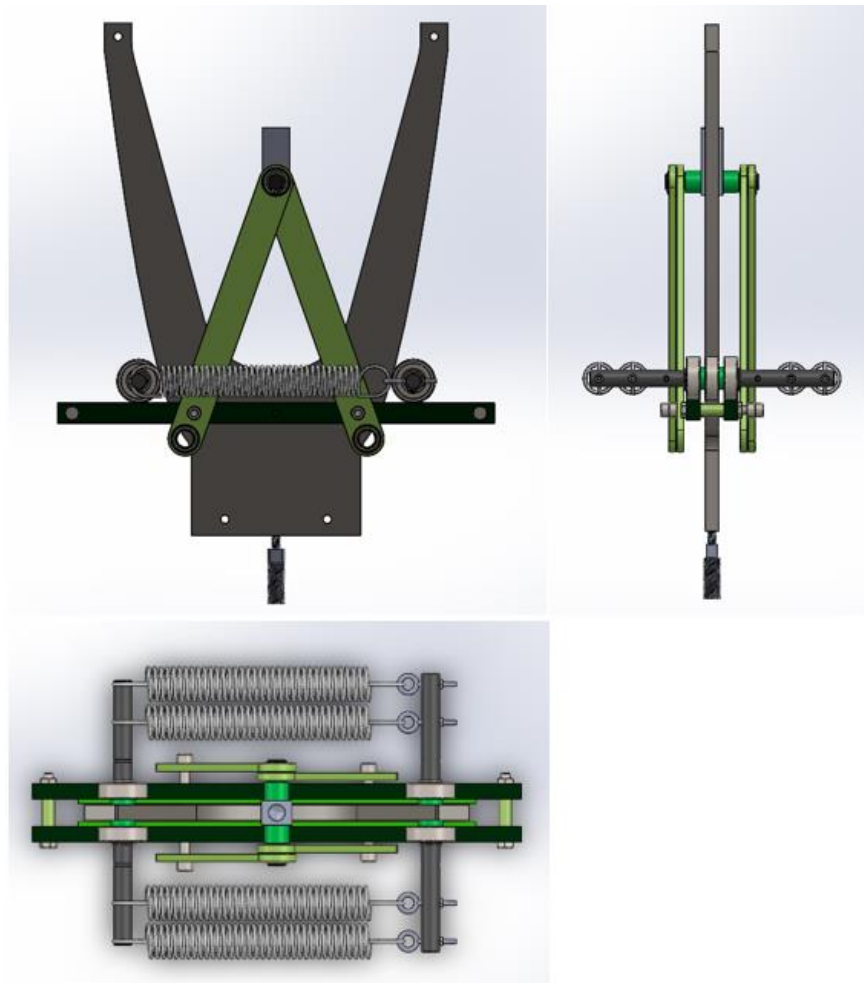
Alzado, planta y perfil del diseño del prototipo MFC-1.
